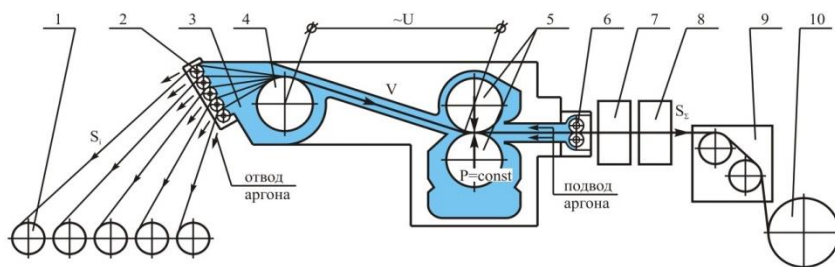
Схема процесса получения многослойной ленты: 1 – рулоны лент-заготовок; 2 – направляющие ролики; 3 - зона с контролируемой атмосферой; 4 – опорный ролик; 5 – обогреваемые валки; 6 – выводные ролики; 7 - измеритель толщины композиции; 8 – измеритель сплошности композиции; 9 - измеритель натяжения; 10 – рулон готовой ленты.
